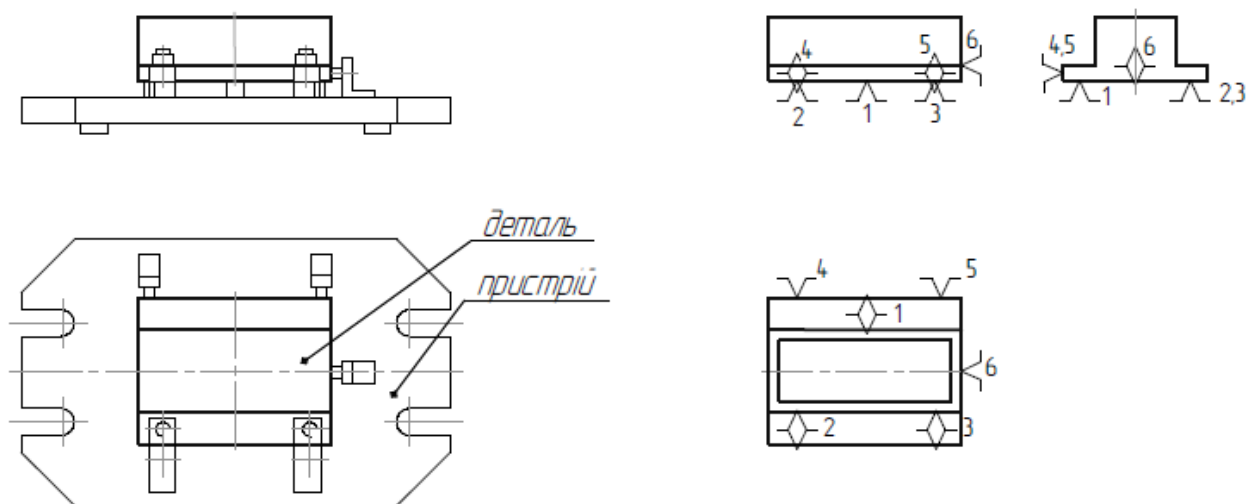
Схема базування корпусної деталі по площині основи і двох бокових поверхнях
